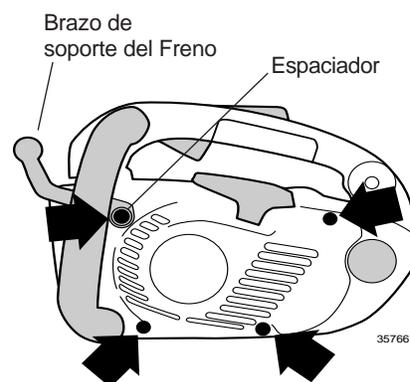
Retirar los Cuatro Tornillos del Arrancador
